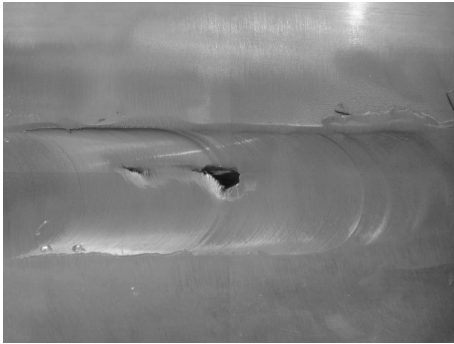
匙孔(未填充)FSW 焊缝形貌
